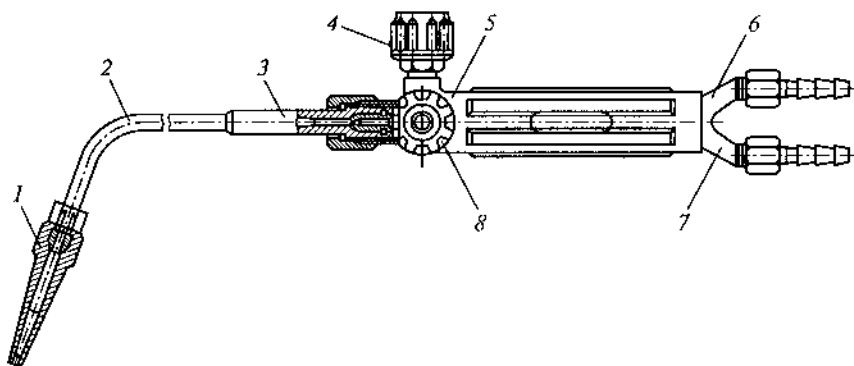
Схема безынекторной сварочной горелки:
